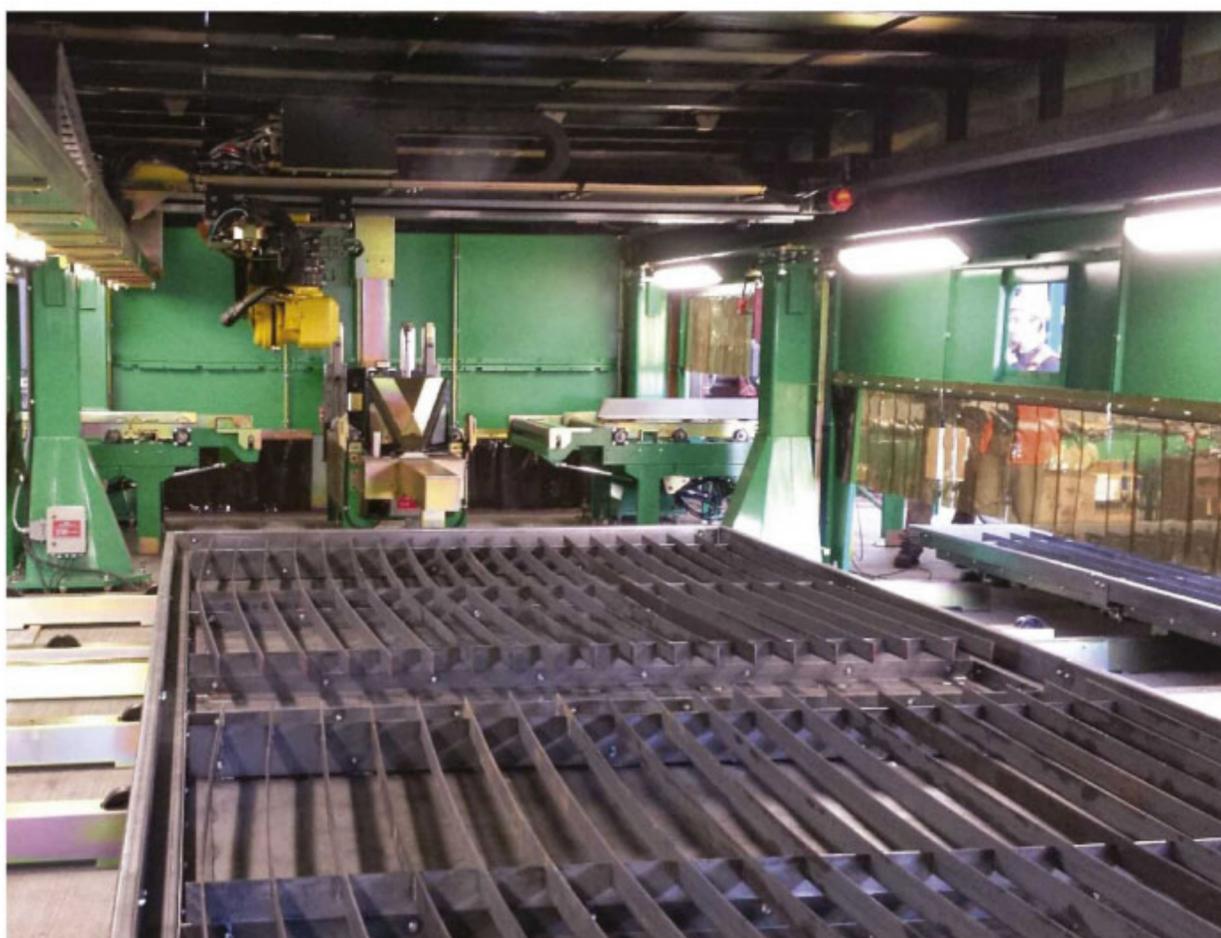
Una vista completa del sistema de Gunderson con la línea de haz robótico en el fondo y la mesa de corte de placas en primer plano.
